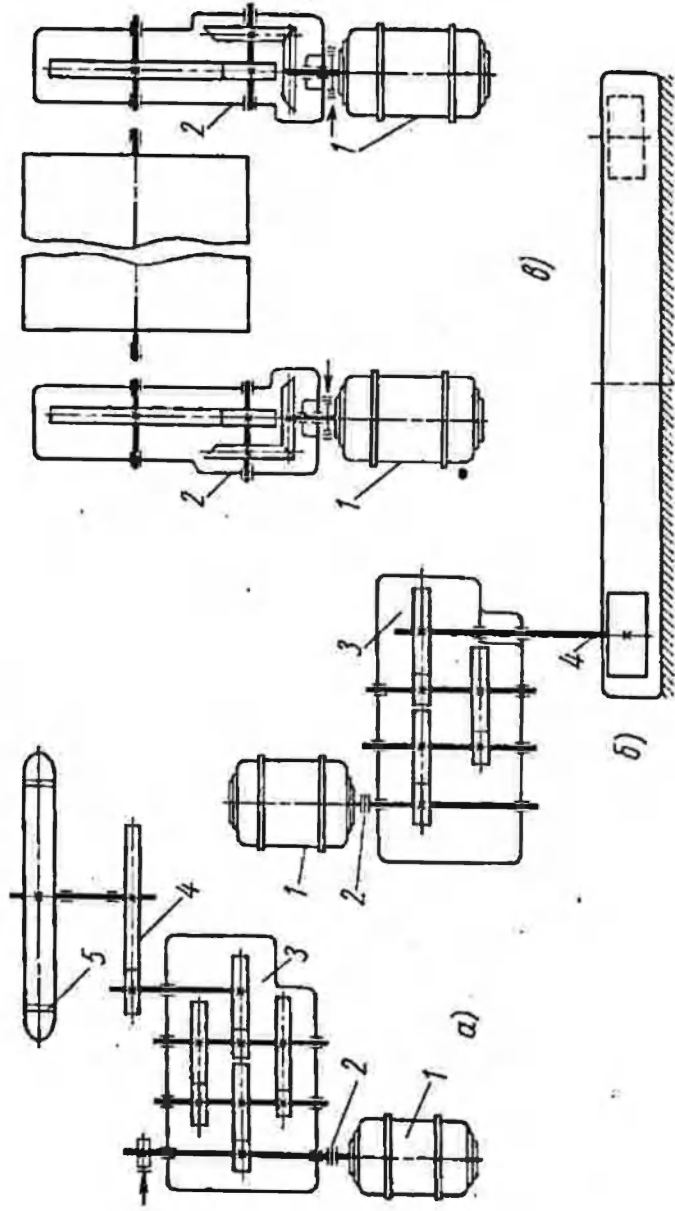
Кинематические схемы привода основных механизмов роторного экскаватора ЭРШР-1600 $\frac{40}{7}$:
